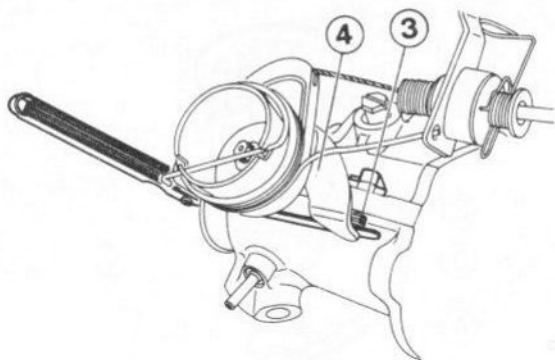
Réglage du contacteur de papillon (Sec 22)
